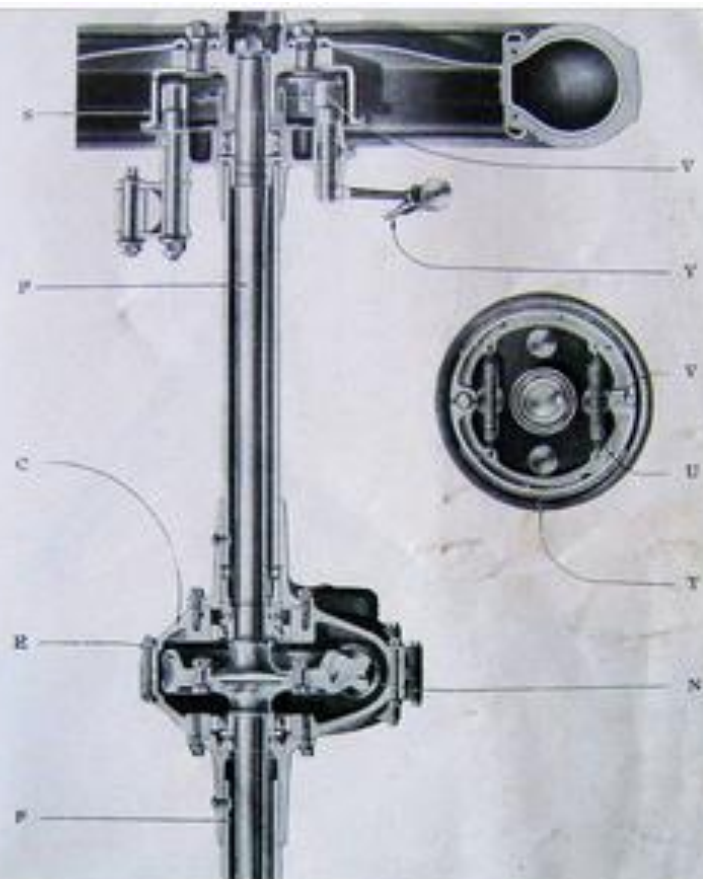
COUPE DU PONT ARRIÈRE ET VUE D'UN FREIN.
